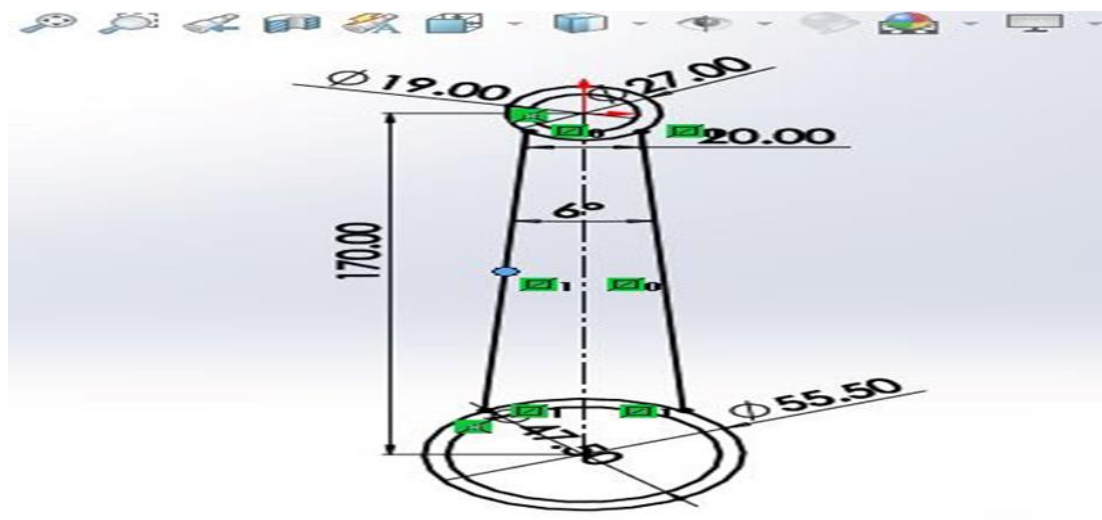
Étape de la construction d'une forme 2D de la bielle
